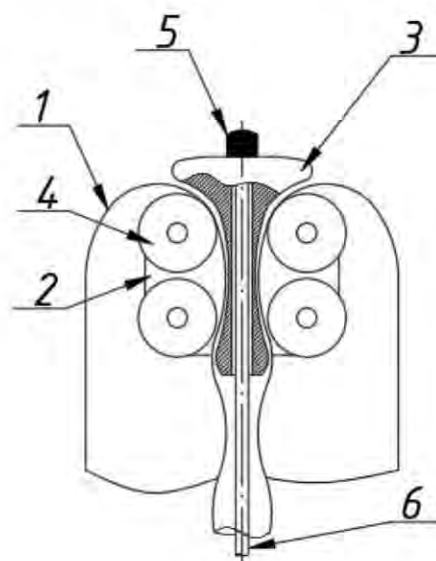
Головка робота: 1 – тіло робота; 2 – внутрішній корпус з роликами; 3 – зовнішній корпус з закріпленою камерою; 4 – ролики; 5 – камера; 6 – кабель живлення камери
